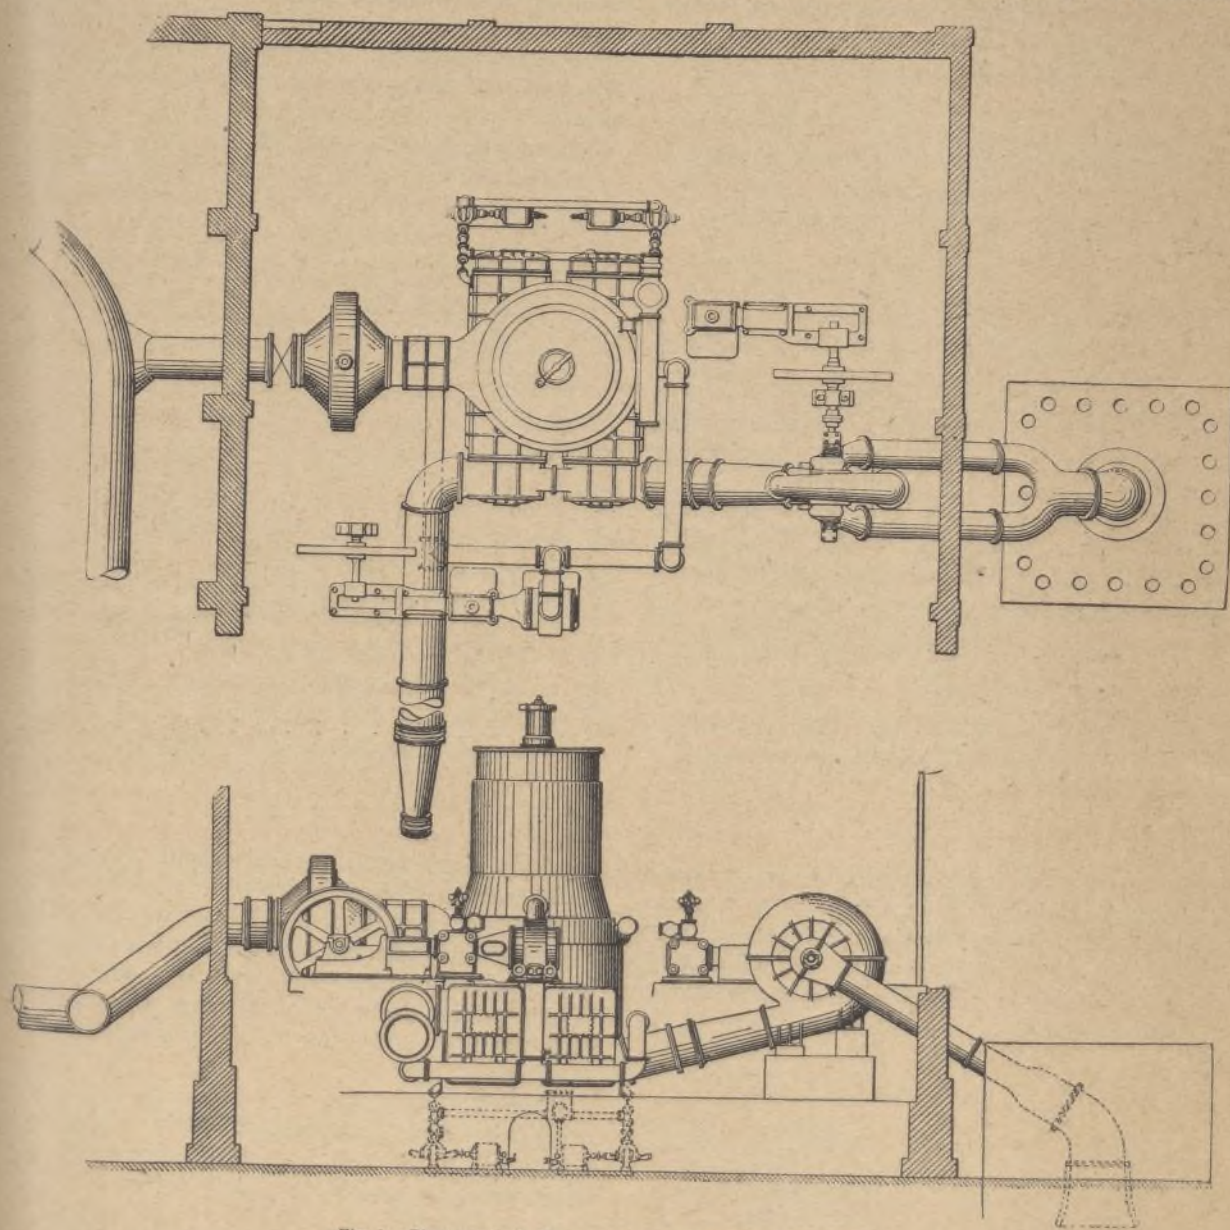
Planta y alzada del condensador y la turbina en conexión.
